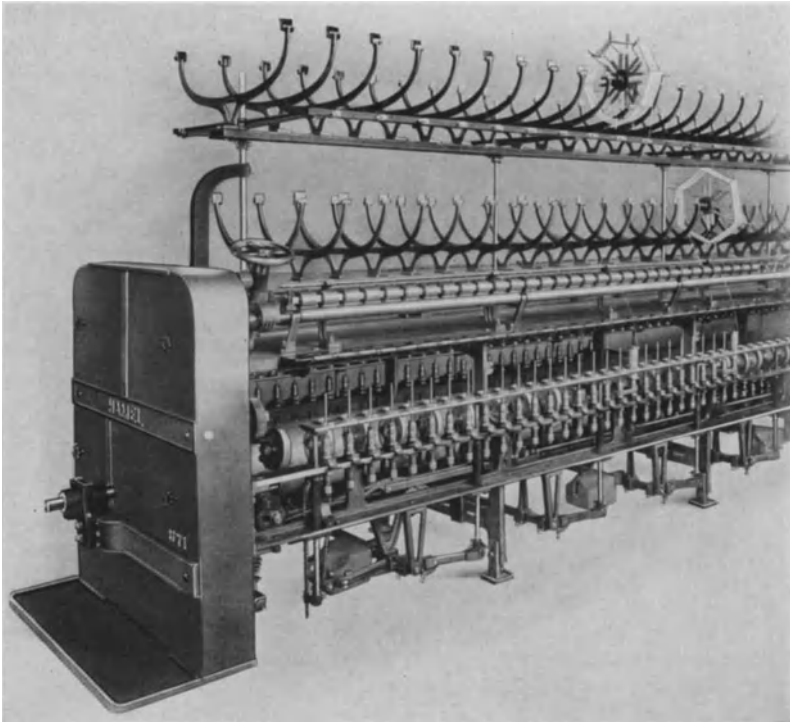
Ringzwirnmachine der Firma Carl Hamel A.G., Chemnitz. Die abgebildete Maschine trägt das Ablaufzeug für Stränge. Dieses entfällt in der Kunstseidenfabrik und wird durch ein solches für Walzen oder Spinnspulen ersetzt.
